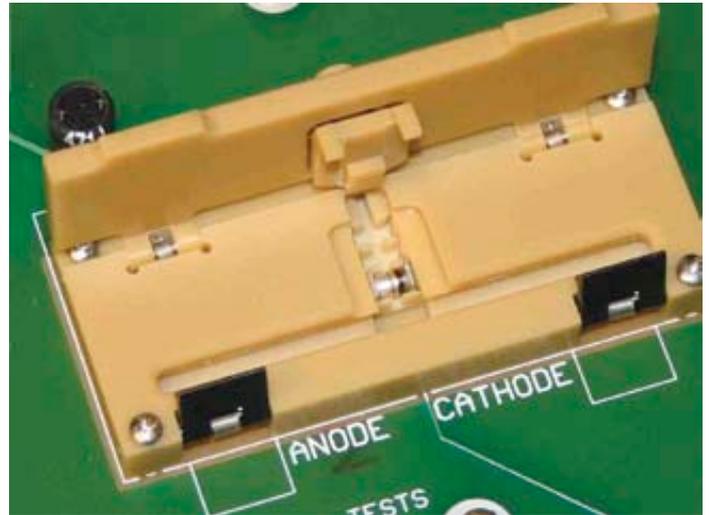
Test-jig contact für die Kontaktierung von Dioden im SQ-MELF-Gehäuse
